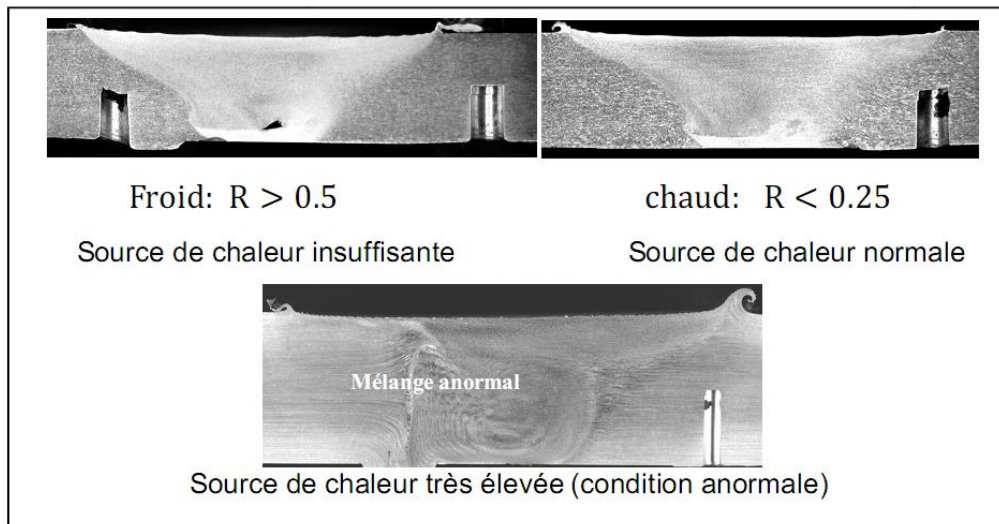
Illustration des conditions de soudage. Cas du soudage de l'aluminium AA7020-T6 (IS)
